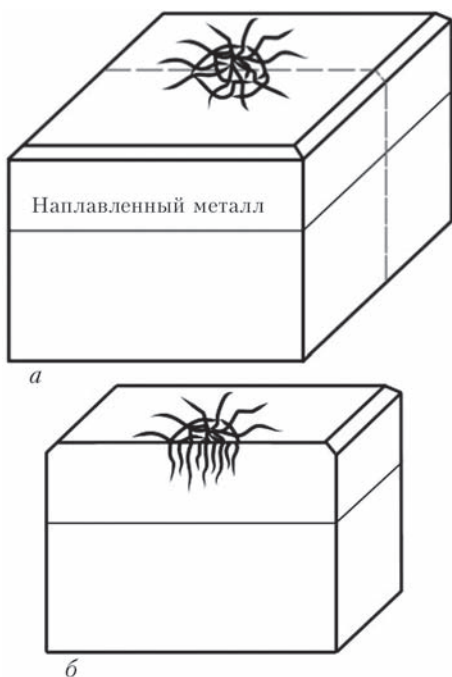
Схема порезки образца для изготовления макрошлифа: а — образец после испытания; б — образец после порезки
